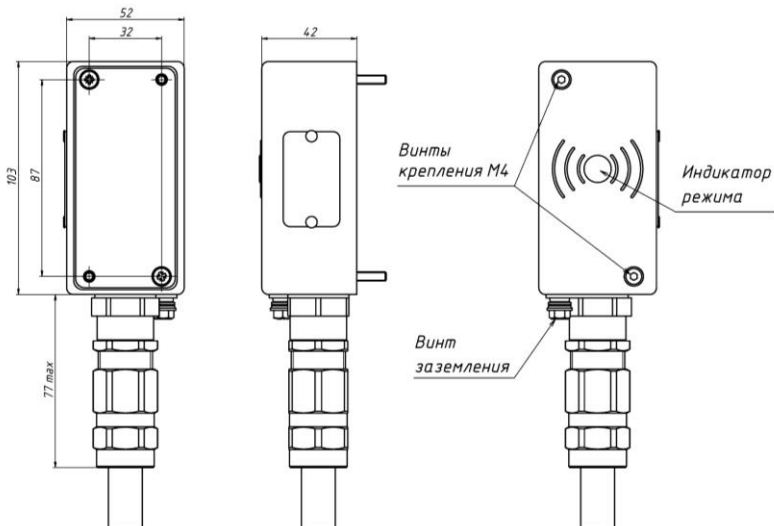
Габаритно-установочные размеры считывателя ALM-RD-S08
